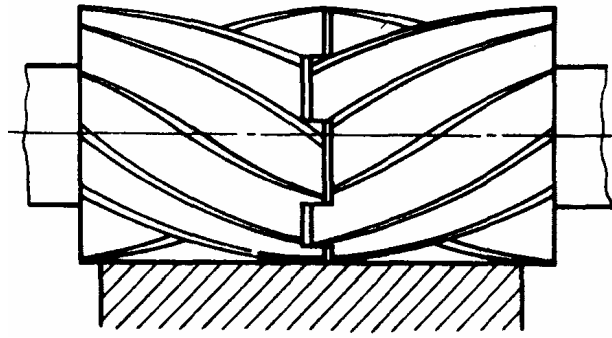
Набір циліндричних фрез для обробки широких поверхонь
